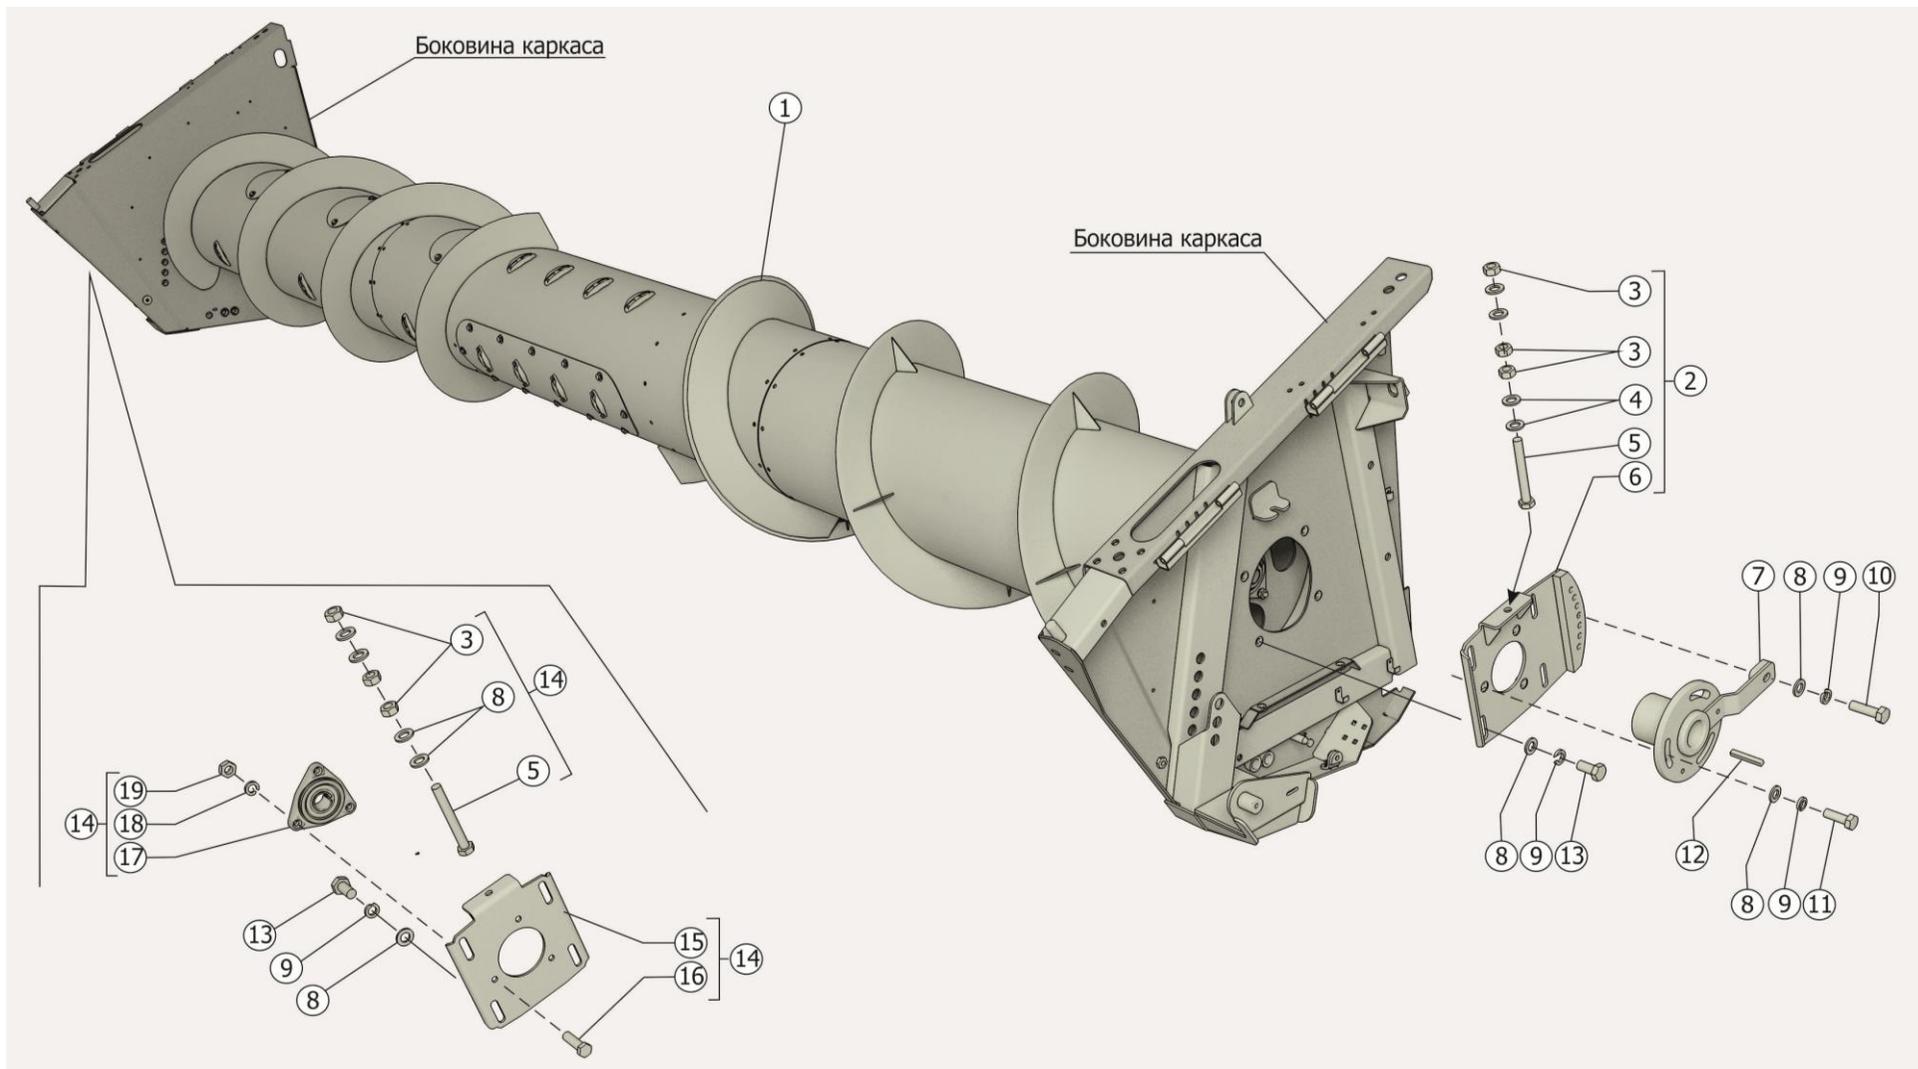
Установка шнека ЖСУ-500.01.01.000А
